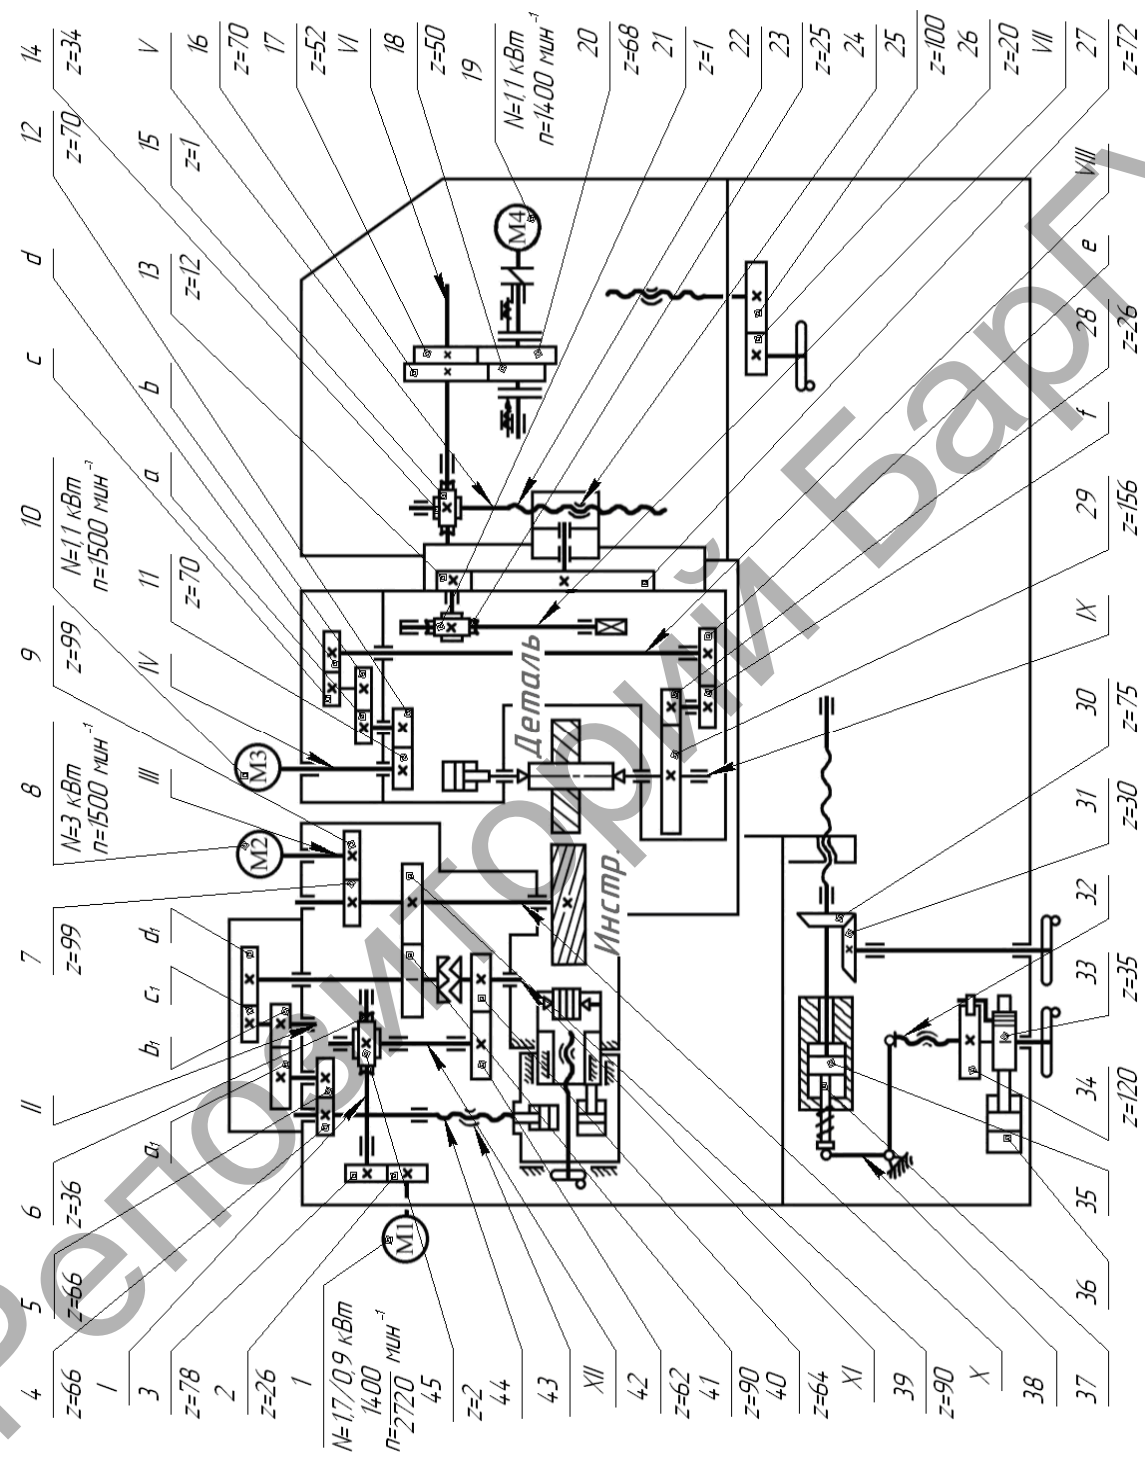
Кинематическая схема зубошлифовального станка модели 5B832
